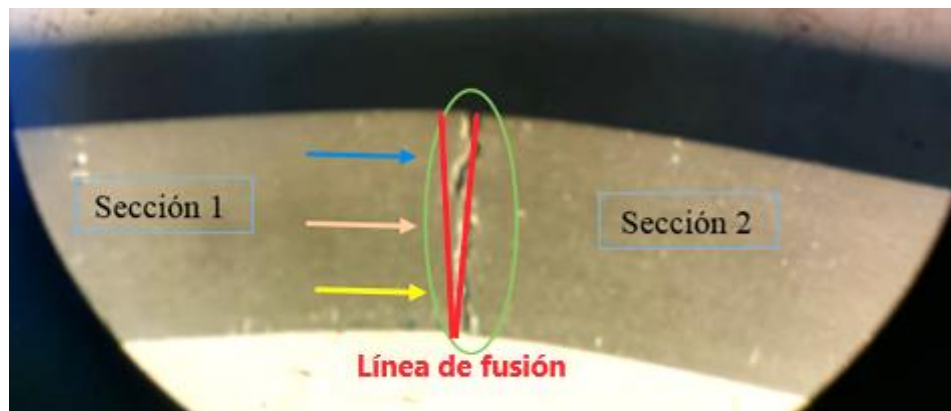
Fotografía de la probeta fracturada por el ensayo de impacto.
